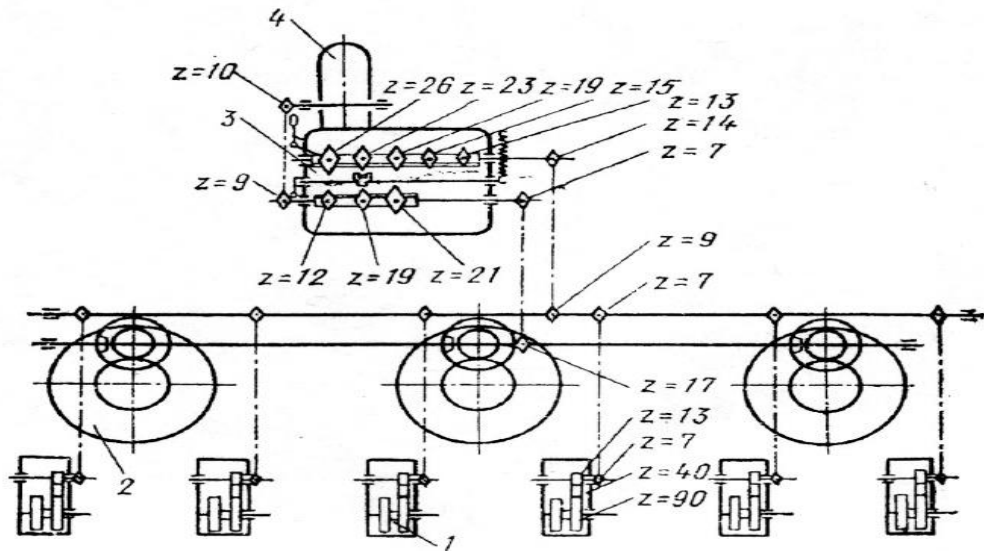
Схема механізму передач сівалки ССТ-12Б
